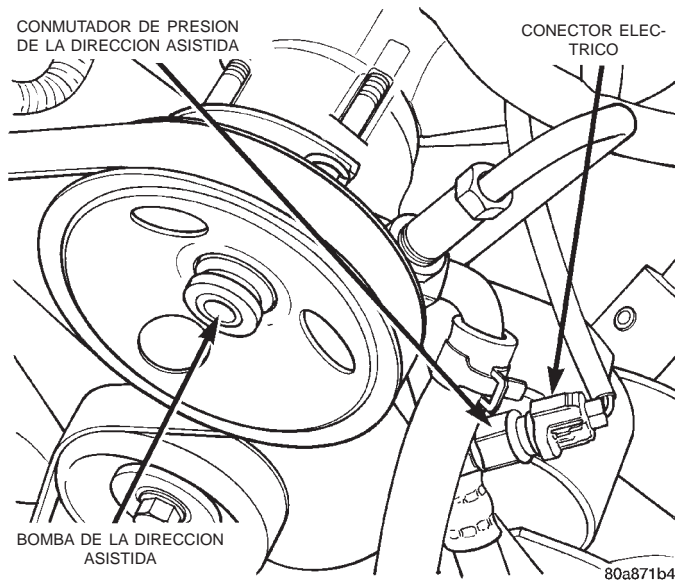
Conmutador de presión de la bomba de la dirección asistida—motor 2.5L
